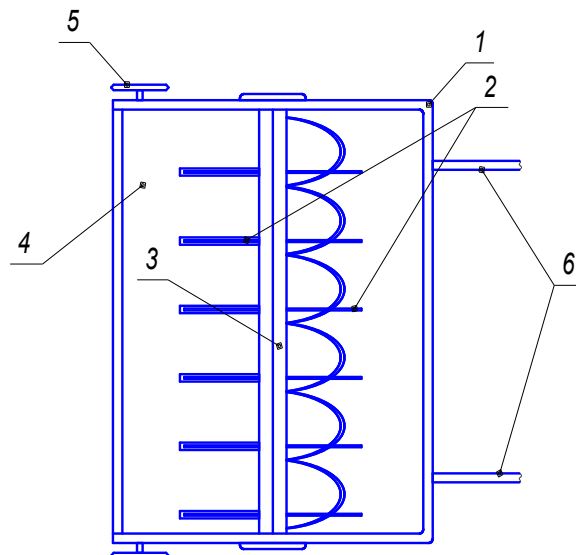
Питатель-разрушитель навоза глубокой подстилки:
